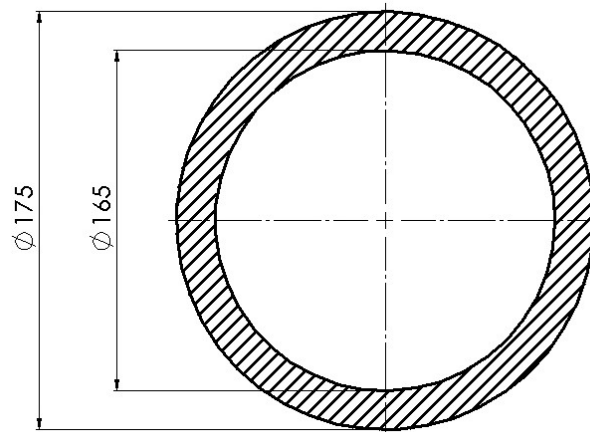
Dimensiones de la sección cilíndrica hueca en mm (Fuente: propia)
